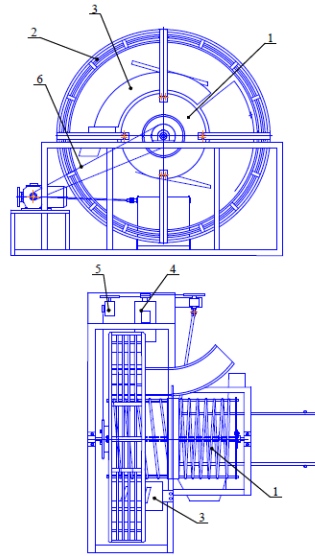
Схема конструкції барабанної сортувальної машини: 1 – сортувальний барабан; 2 – ротор-живильник; 3 – приймальний лоток; 4 – електродвигун; 5 – редуктор; 6 – ланцюгова передача
